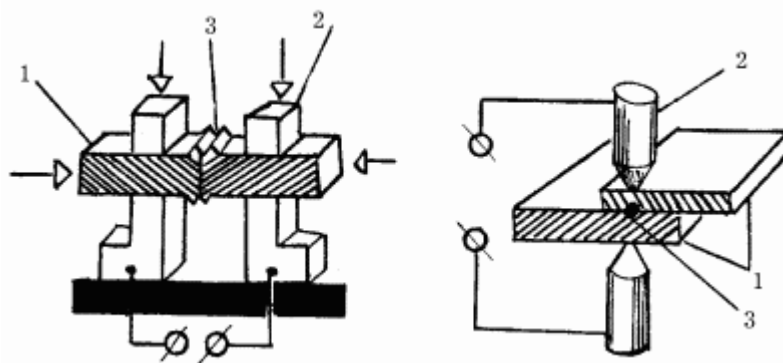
Контактная сварка: 1 – соединяемые заготовки; 2 – электроды; 3 – зона контакта.
